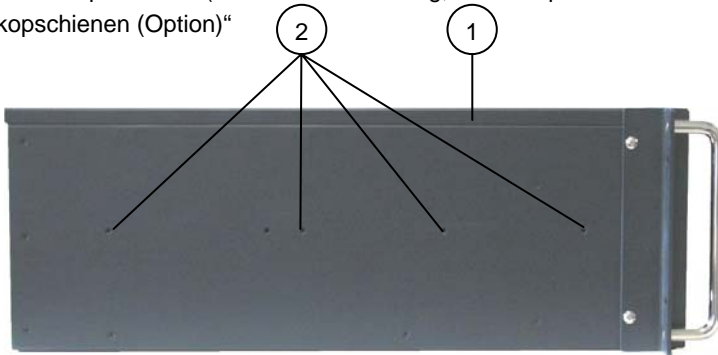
Gewindebohrungen (M4) für Befestigung einer Teleskopschiene
